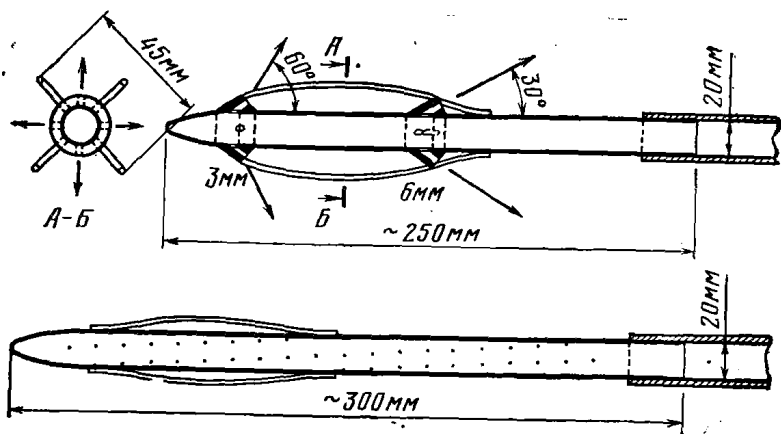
Чертеж струйчатой трубы промывного аппарата [10.2]: вверху — для промывки назад; внизу — для промывки в сторону (масштаб не соблюден); внутренний диаметр труб 20 мм.
